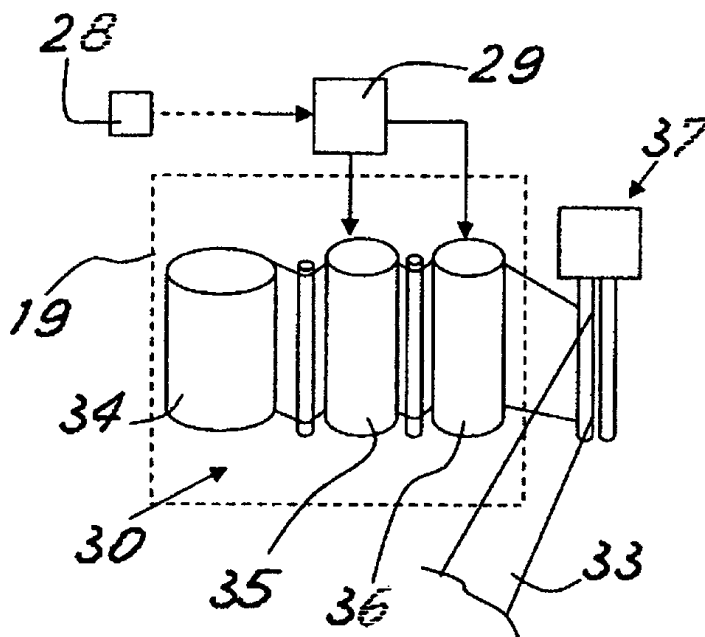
Схематический вид детали для разматывания и раздачи полосы пленки
